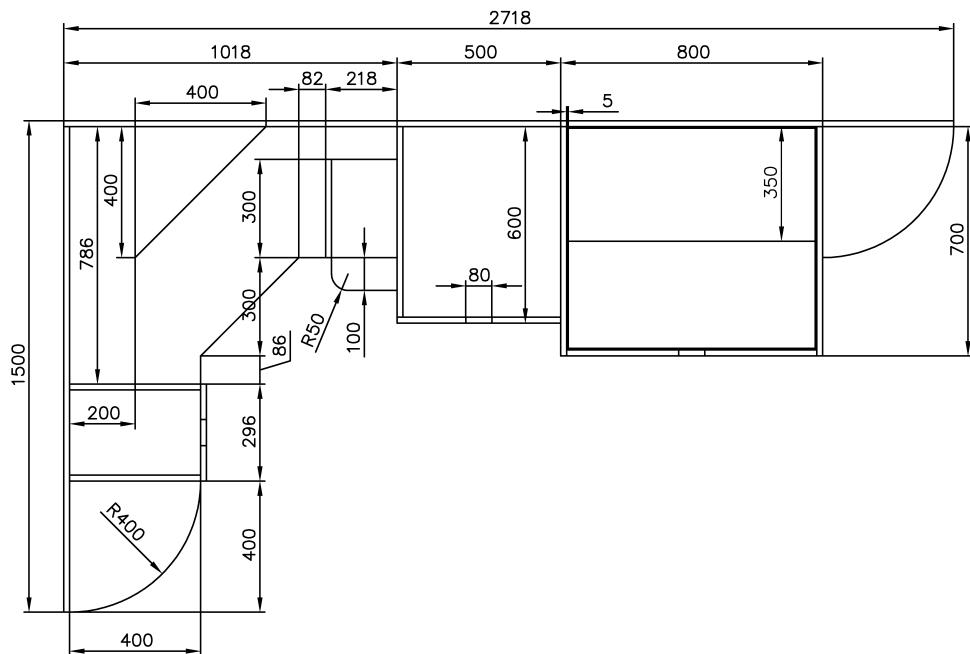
▼ Чертеж нижней части рабочей зоны с основными размерами конструктивных элементов
